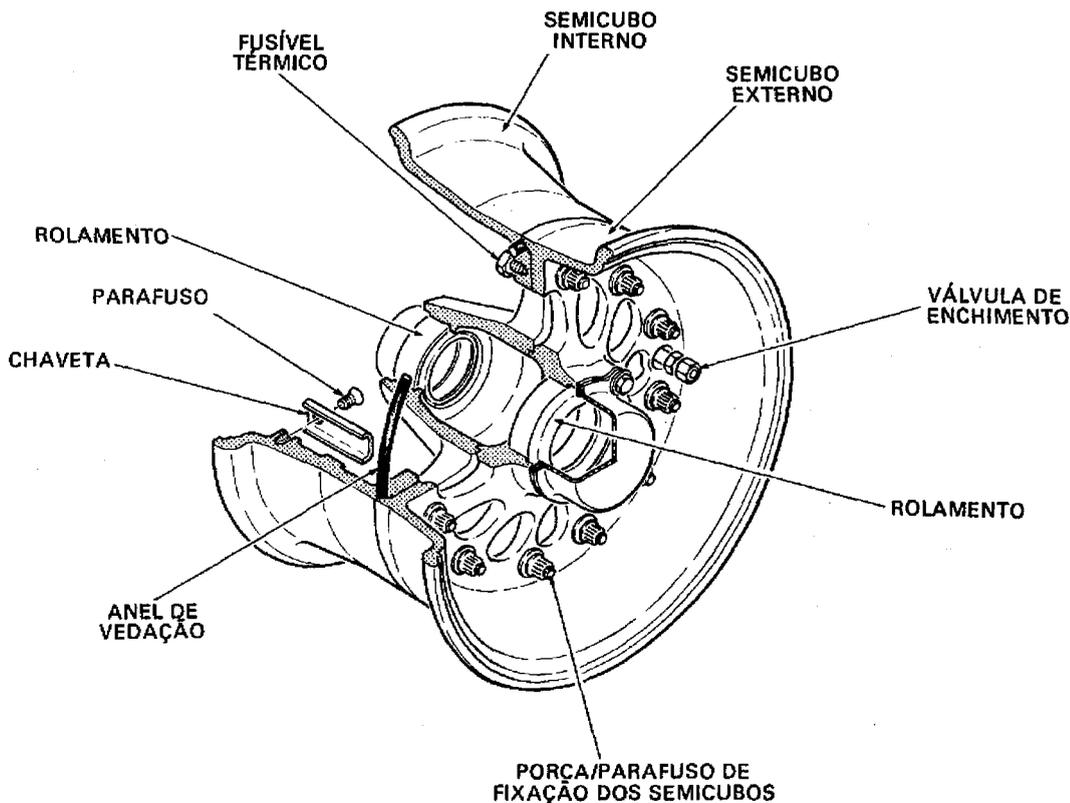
Roda do Trem de Pouso Principal (B.F. GOODRICH)
